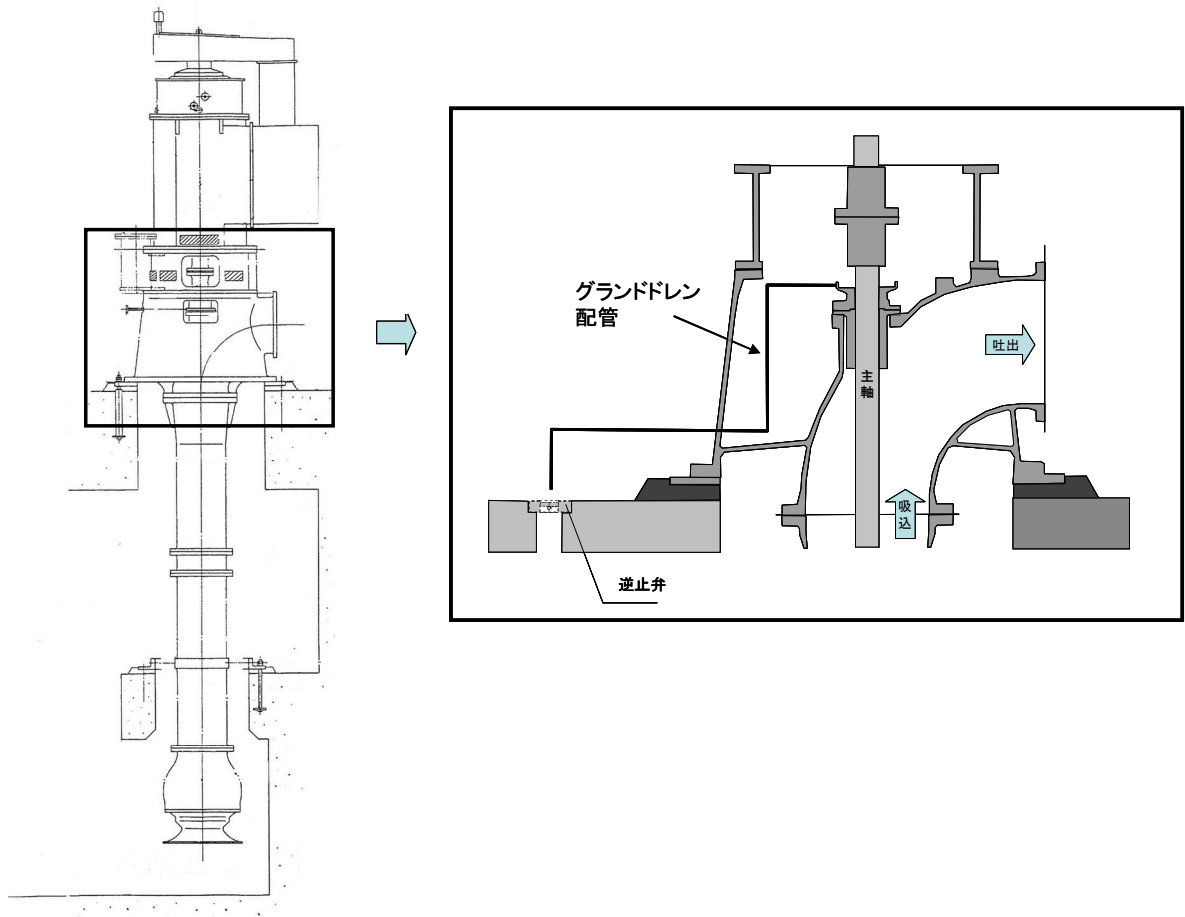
3,4号炉海水ポンプグランド dren 配管ルート
